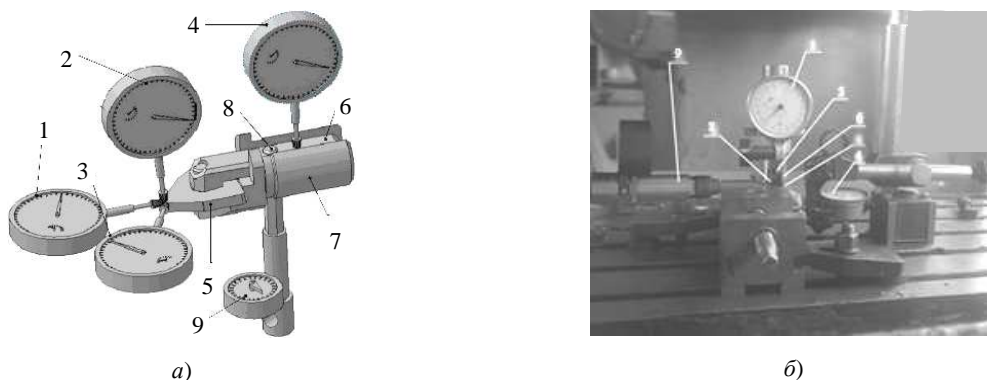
3D-модель (а) и экспериментальная установка (б) для измерения перемещений пластины режущей и прихвата: 1, 2, 3, 4 – индикаторы часового типа; 5 – пластина режущая; 6 – прихват; 7 – блок резцовый; 8 – винт зажимной; 9 – динамометрический ключ
